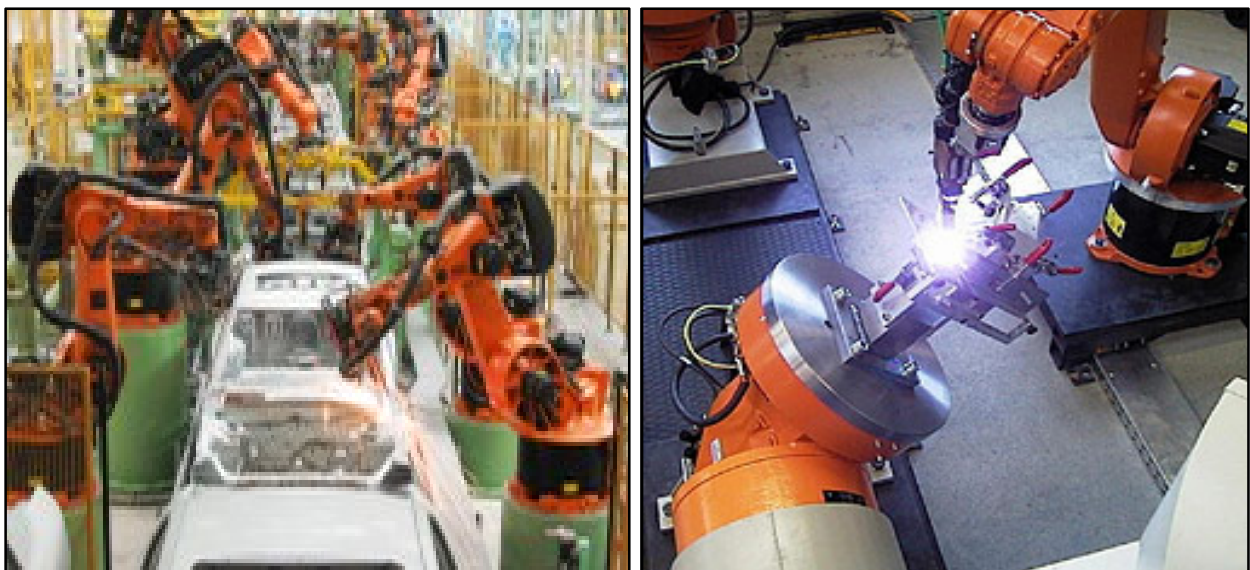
Robots Industriels de Soudage [Rob_source]
